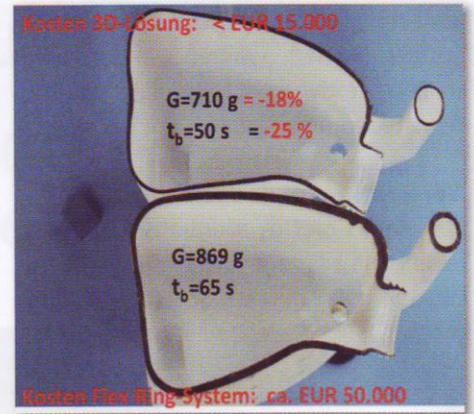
Kanister, hergestellt mit konventioneller Technik (unten) und 3D Technik (oben) [G = Gewicht des Kanisters; t_b = Blas- bzw. Kühlzeit]
